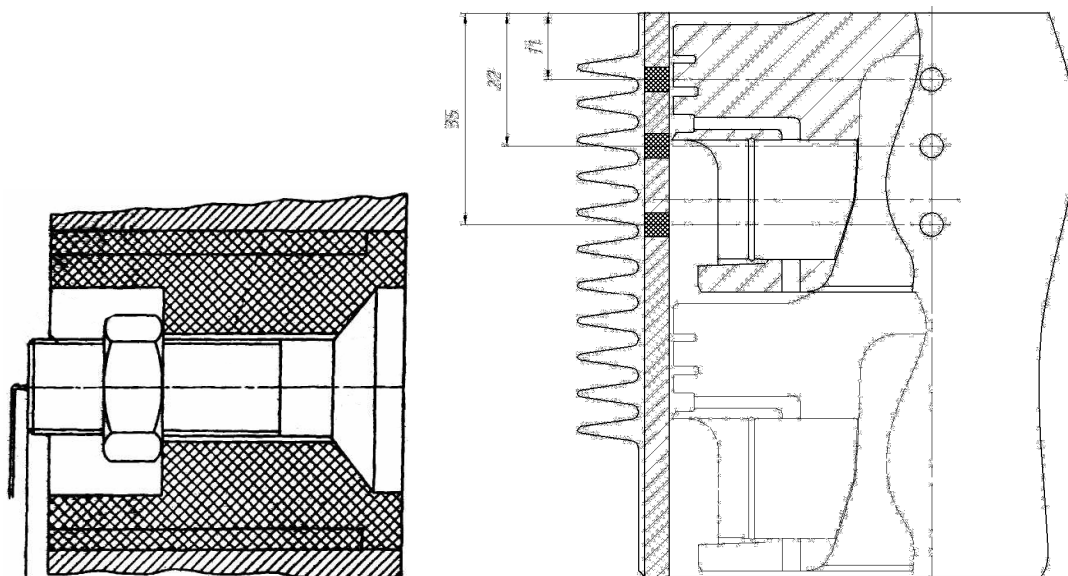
Конструкция датчиков толщины масляного слоя и установка их в цилиндре двигателя
